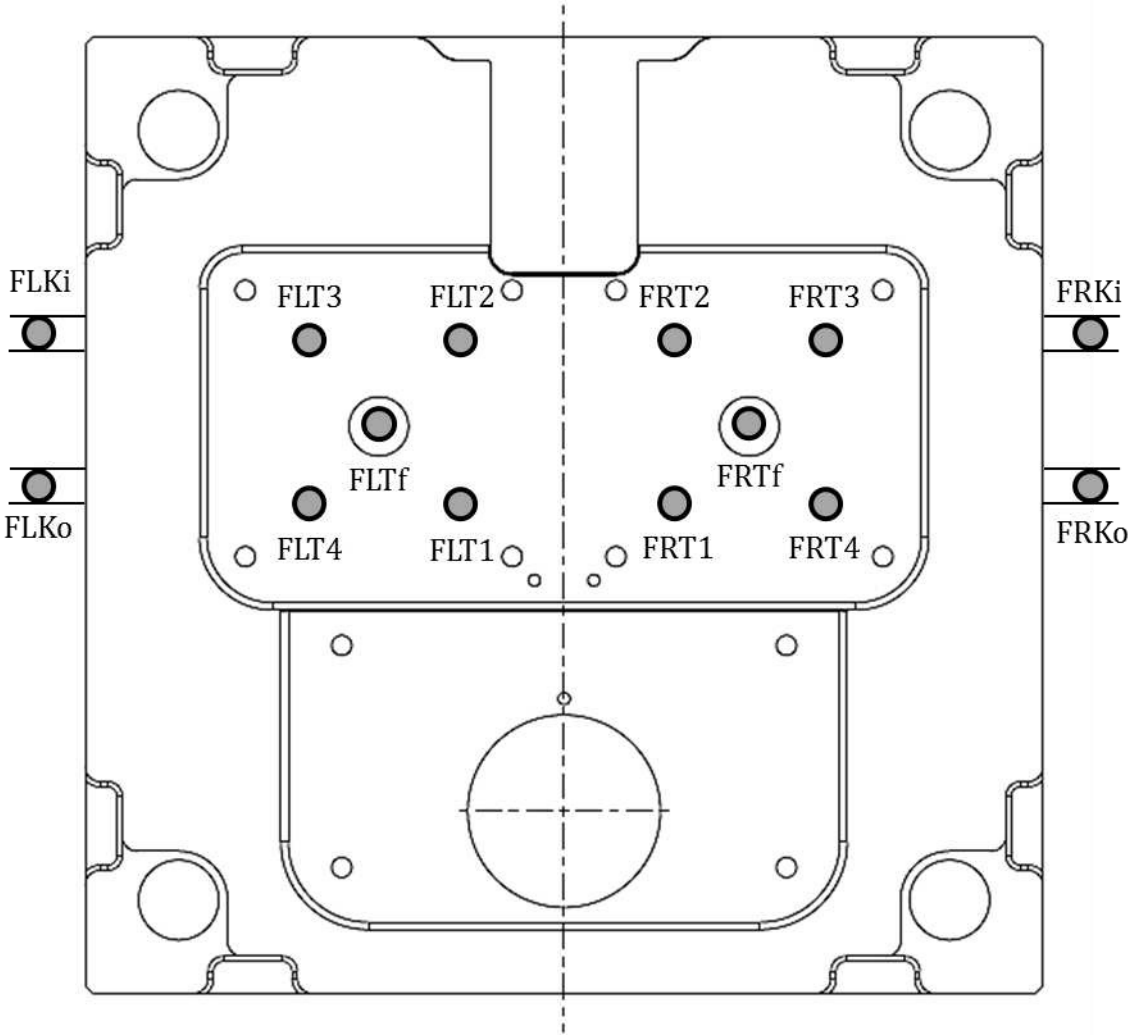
Messstellen in der festen Werkzeughälfte des Zwillingplatten-Werkzeugs.
